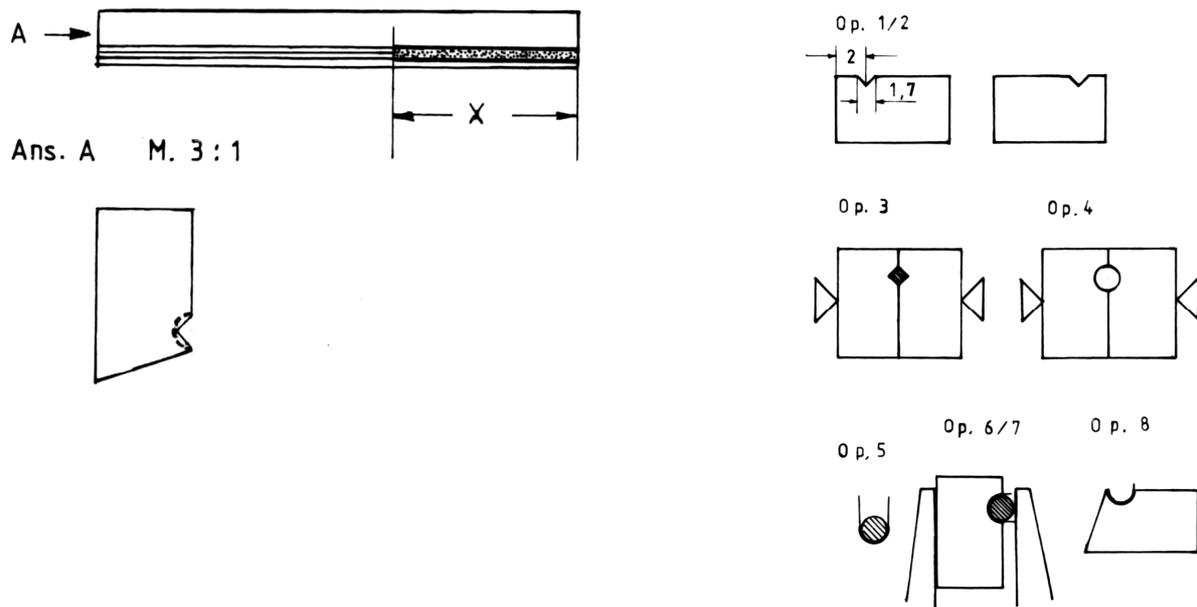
Formwerkzeug - x = Länge des vorhandenen Bohrers. Abb. 11: Herstellung des Formwerkzeuges - Op. 1-8
